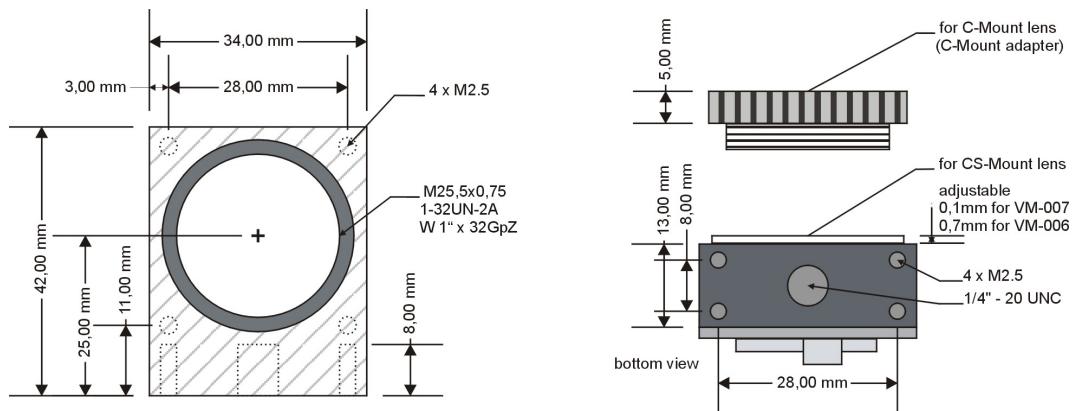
Abmessungen phyCAM mit C/CS-Mount Halter
